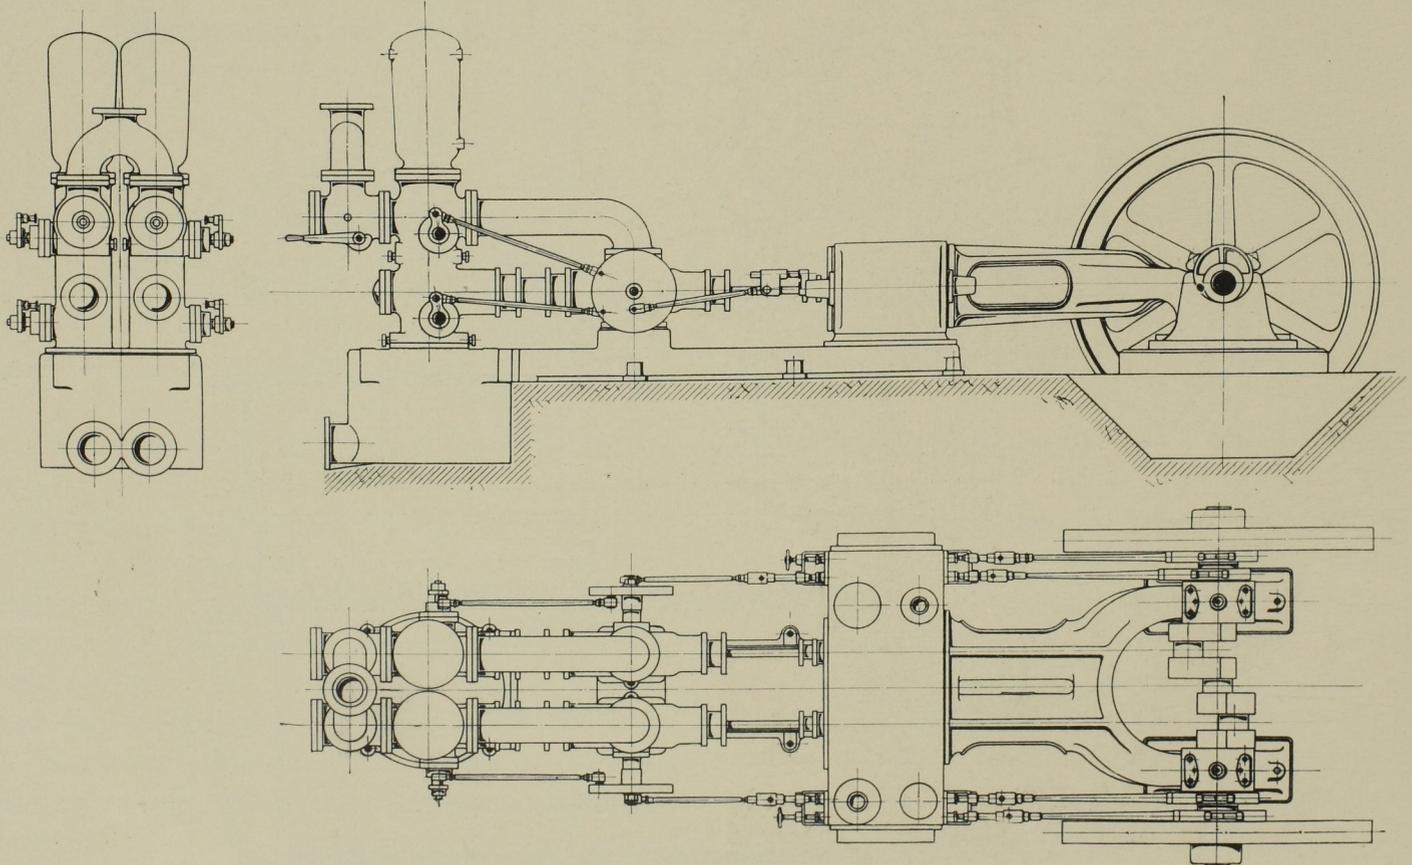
Grundriss, Seiten- und Rückansicht der Maschine. Masst. 1 : 48.
